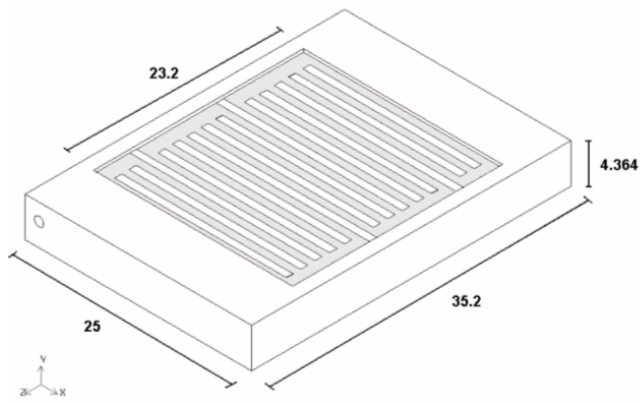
Dimensiones del diseño de serpentin triple. (mm)
